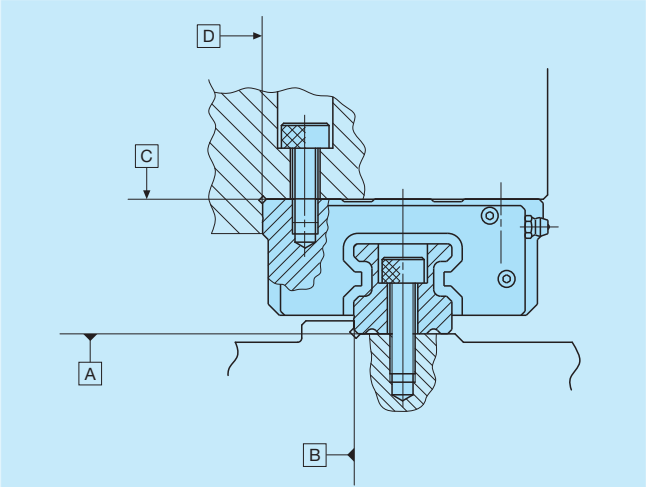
Superfície de montagem de referência e estrutura de montagem típica
